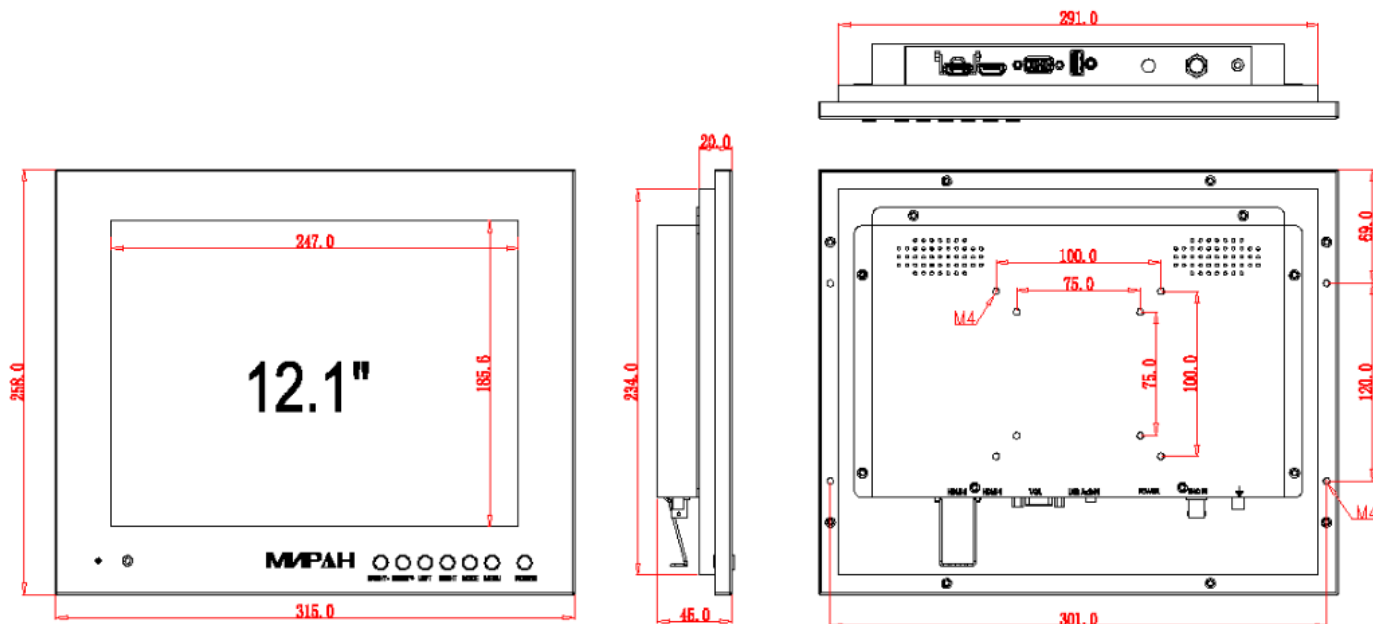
Габаритный чертеж монитора ИВМ-12ЖК.
